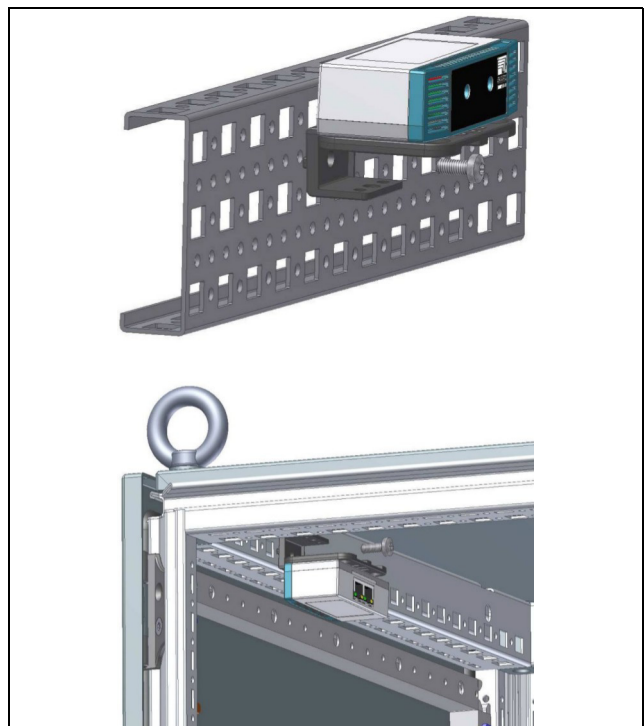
Befestigen des Sensors im Schaltschrank bzw. IT-Schrank
